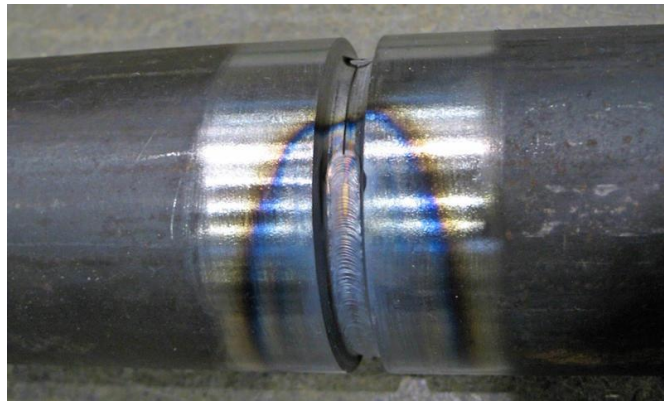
Zona afectada térmicamente por la soldadura.
